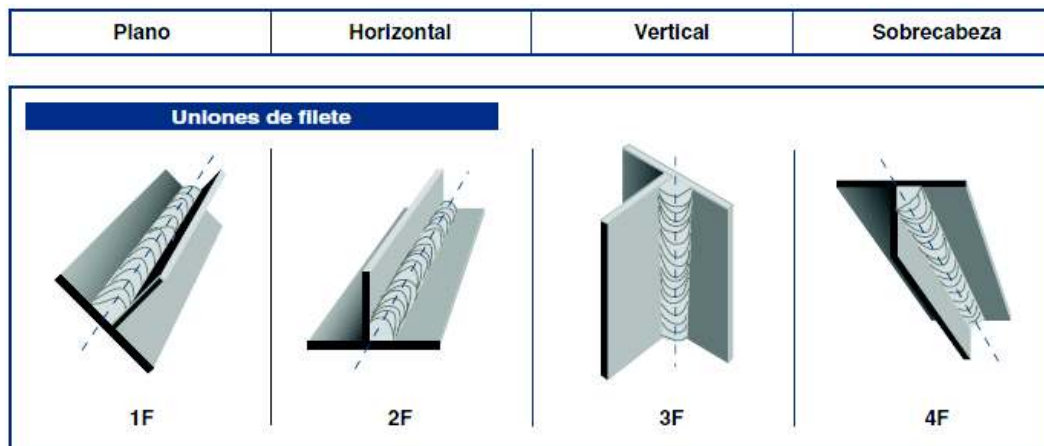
Posiciones de soldadura para uniones de filete⁴⁶
